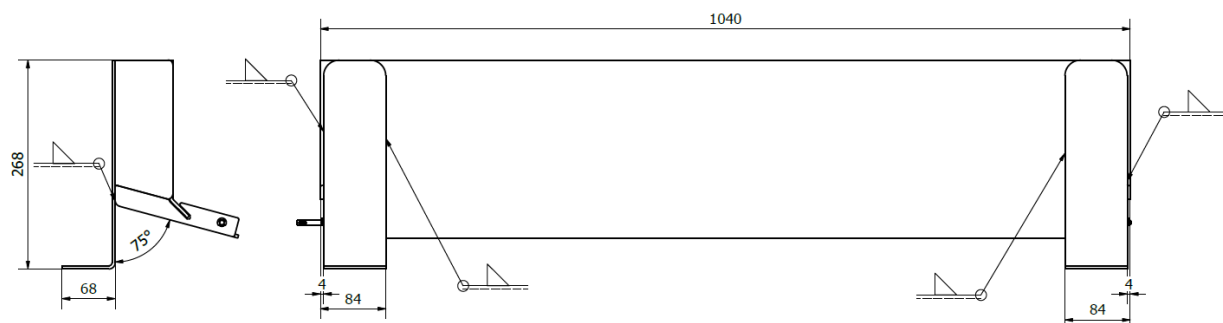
Representação do esquema de soldadura do reservatório, medidas em milímetros e simbologia normalizada para soldadura.
